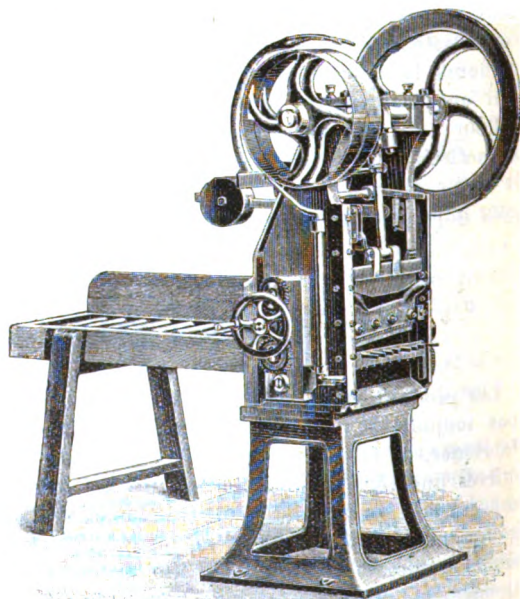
MACHINE A DÉCOUPER LES COPEAUX EN TIGES.
